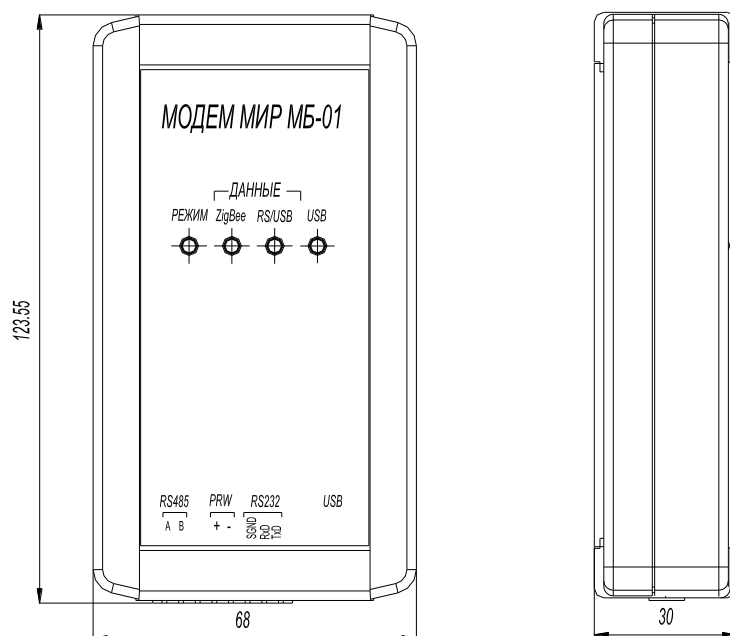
Внешний вид и габаритные размеры модема МБ-01
